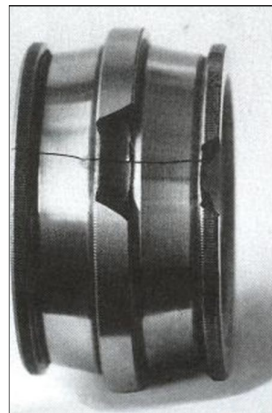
80.-Fractura del aro interior de un rodamiento de rodillos a rótula. Uno de los rodillos ha sido extraído para permitir que el camino de rodadura en el lado izquierdo fuese examinado. El rodillo fue reinsertado con el martillo causando parte de la rotura de la pestaña central. Los impactos han sido transmitidos al camino opuesto a través de un rodillo, y parte de la pestaña también ha saltado. Al mismo tiempo el aro se ha fracturado transversalmente.
